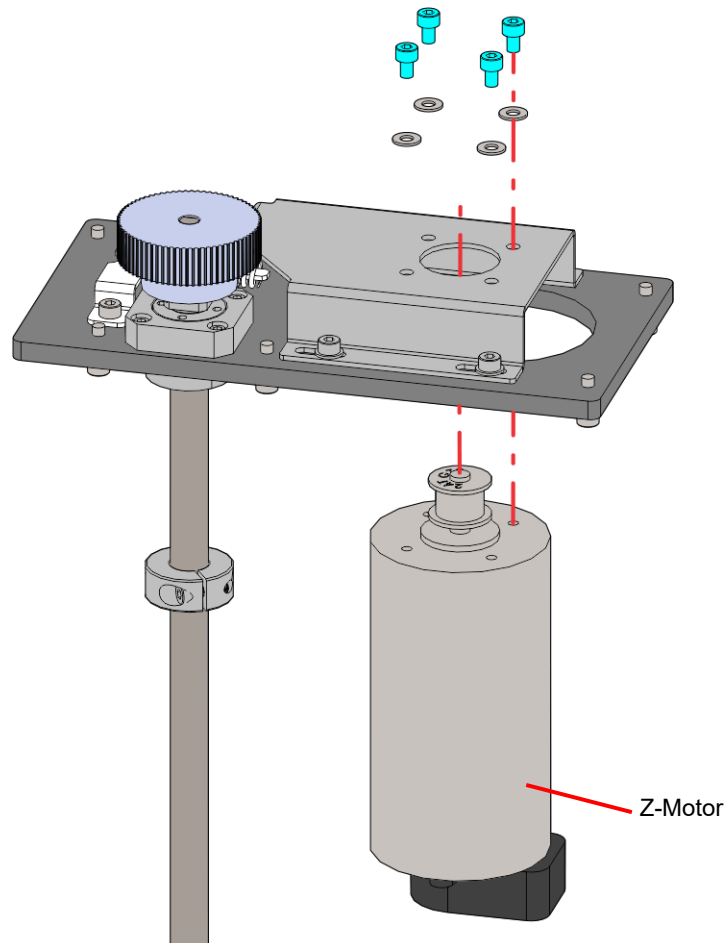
Positionen der Schrauben der Z-Motor-Spannhalterung
